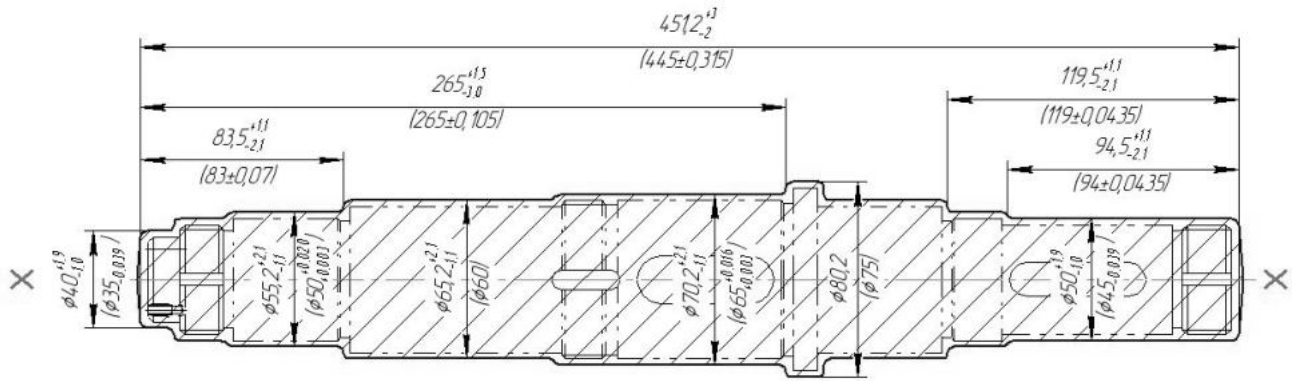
Ескіз заготовки, отриманої методом штампування
